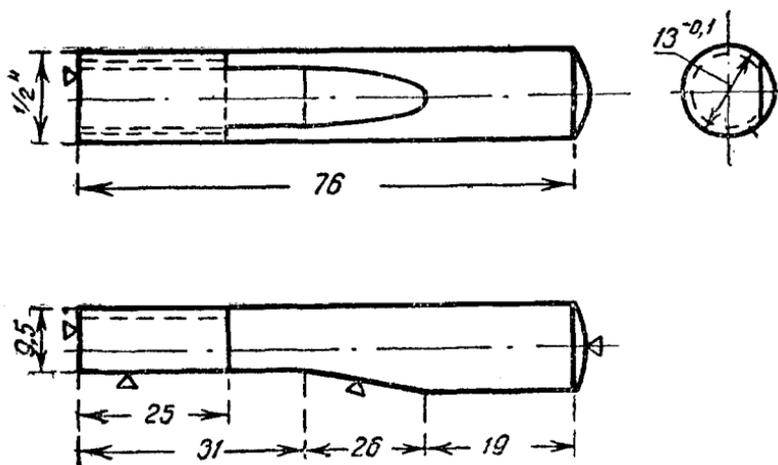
Дет. 15. Установочный болт поворотного кулака
